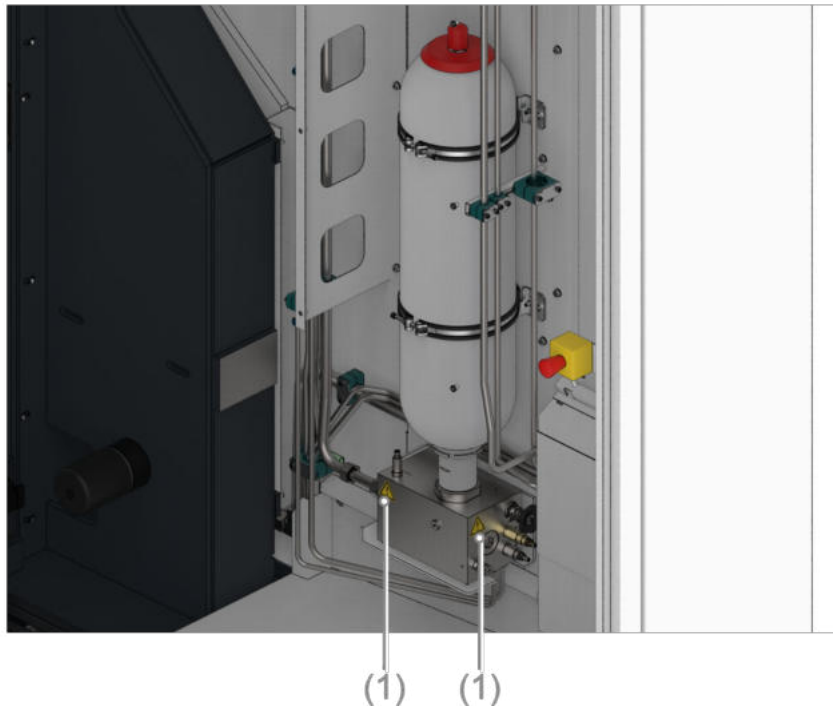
Steuerblock des Gewichtsausgleichs im Maschinenraum
